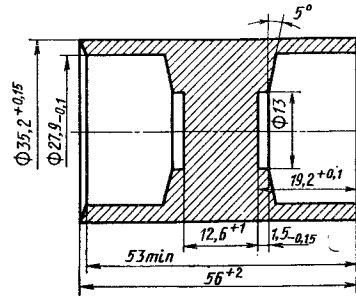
Штампованная заготовка для двух корпусов карданного подшипника
